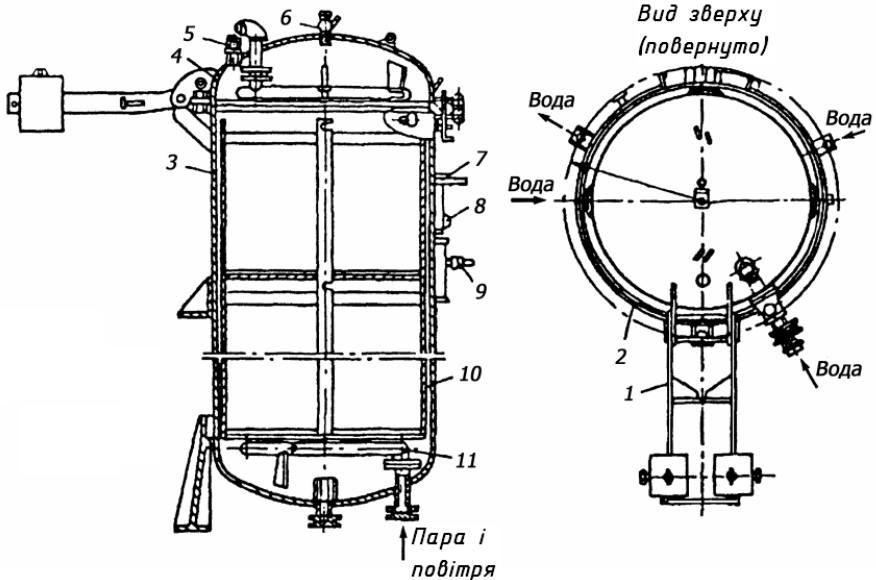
Стерилізатор (автоклав) АВ-4: 1 – зрівноважуючий пристрій; 2 – швидкодіючий затискач; 3 – корпус; 4 – кришка; 5 – запобіжний клапан; 6 – контрольно-спусковий кран; 7 – термометр; 8 – манометр; 9 – програмний регулятор; 10 – корзини; 11 – паровий барботер.
